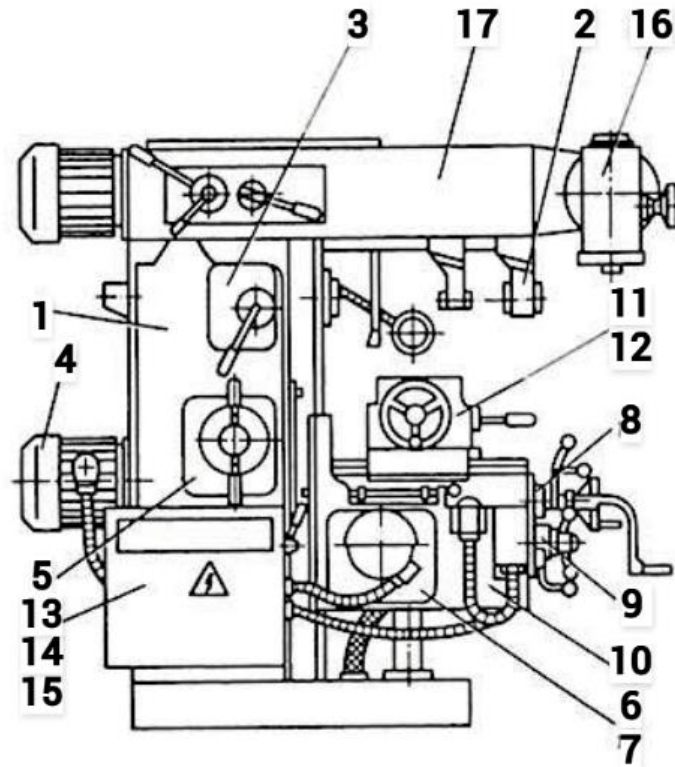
Розташування складових частин консольно-фрезерного верстата 6P81Г
